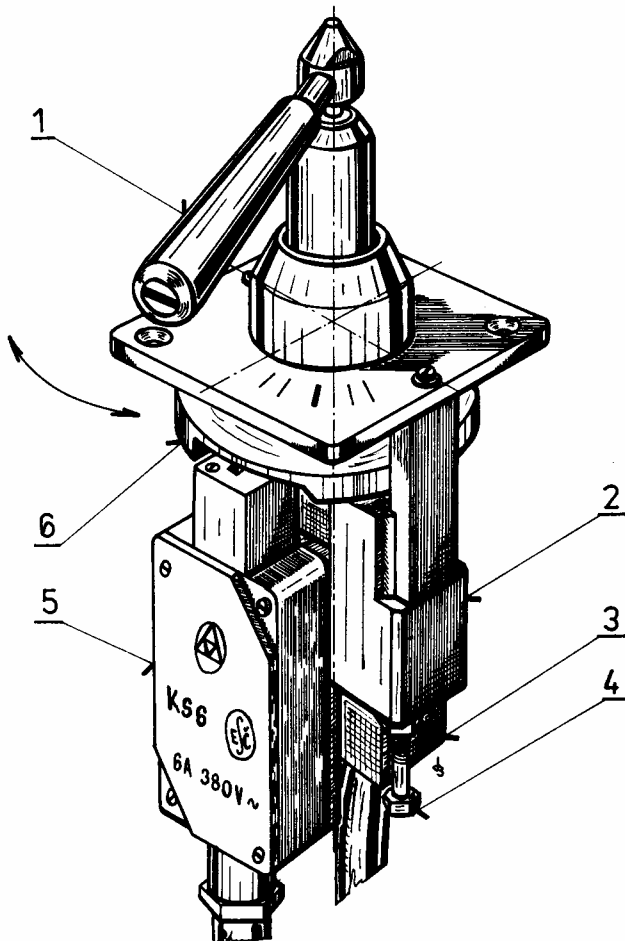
Ovladač elektricky řízené přímočinné brzdy (starší provedení)
